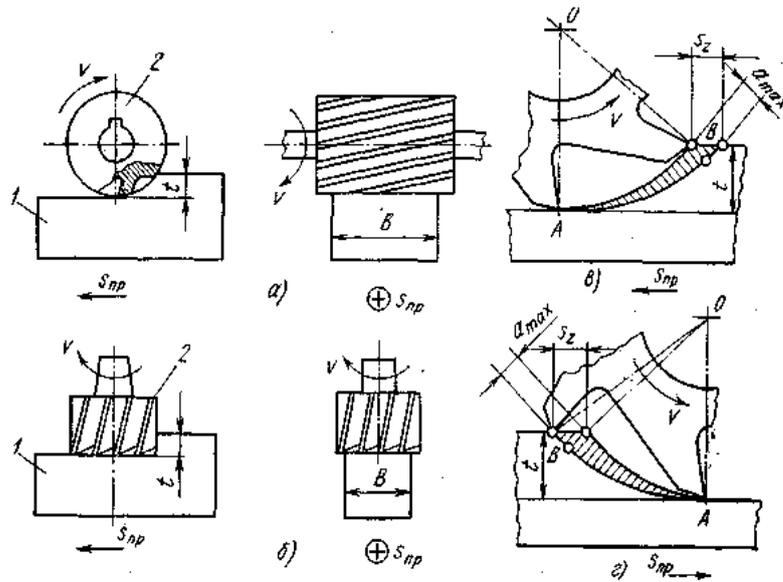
Схемы фрезерования цилиндрической (а) и торцевой (б) фрезами.
